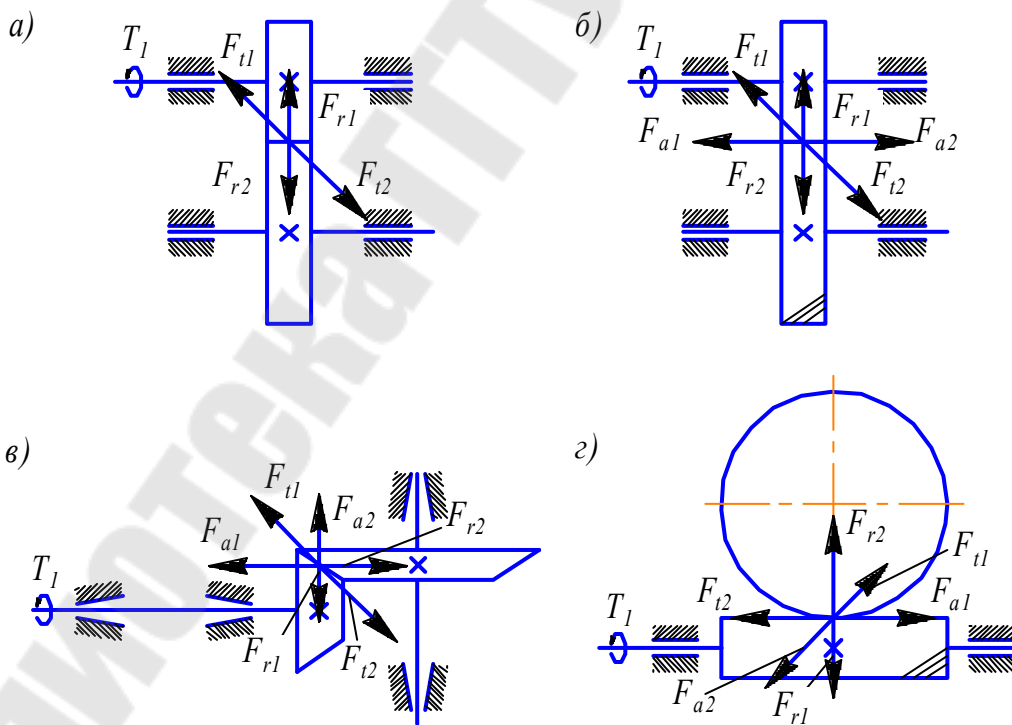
Схема усилий в зубчатых и червячной передачах
